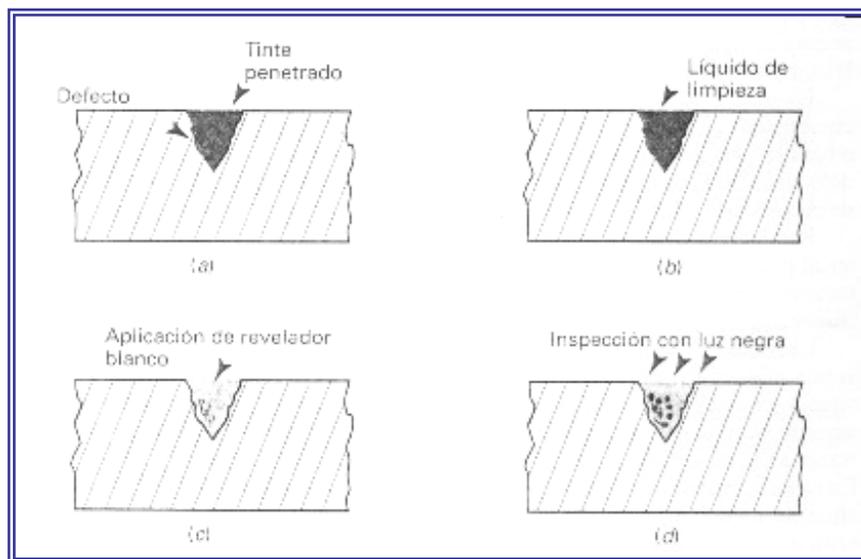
La inspección por líquido penetrante implica cuatro pasos para revelar un defecto: a) se aplica un tinte rojo y se le permite penetrar en un defecto sospechado; b) el exceso de tinte se elimina de la superficie; c) se aplica un revelador blanco; d) la inspección con luz negra muestra en rojo la situación del defecto.
